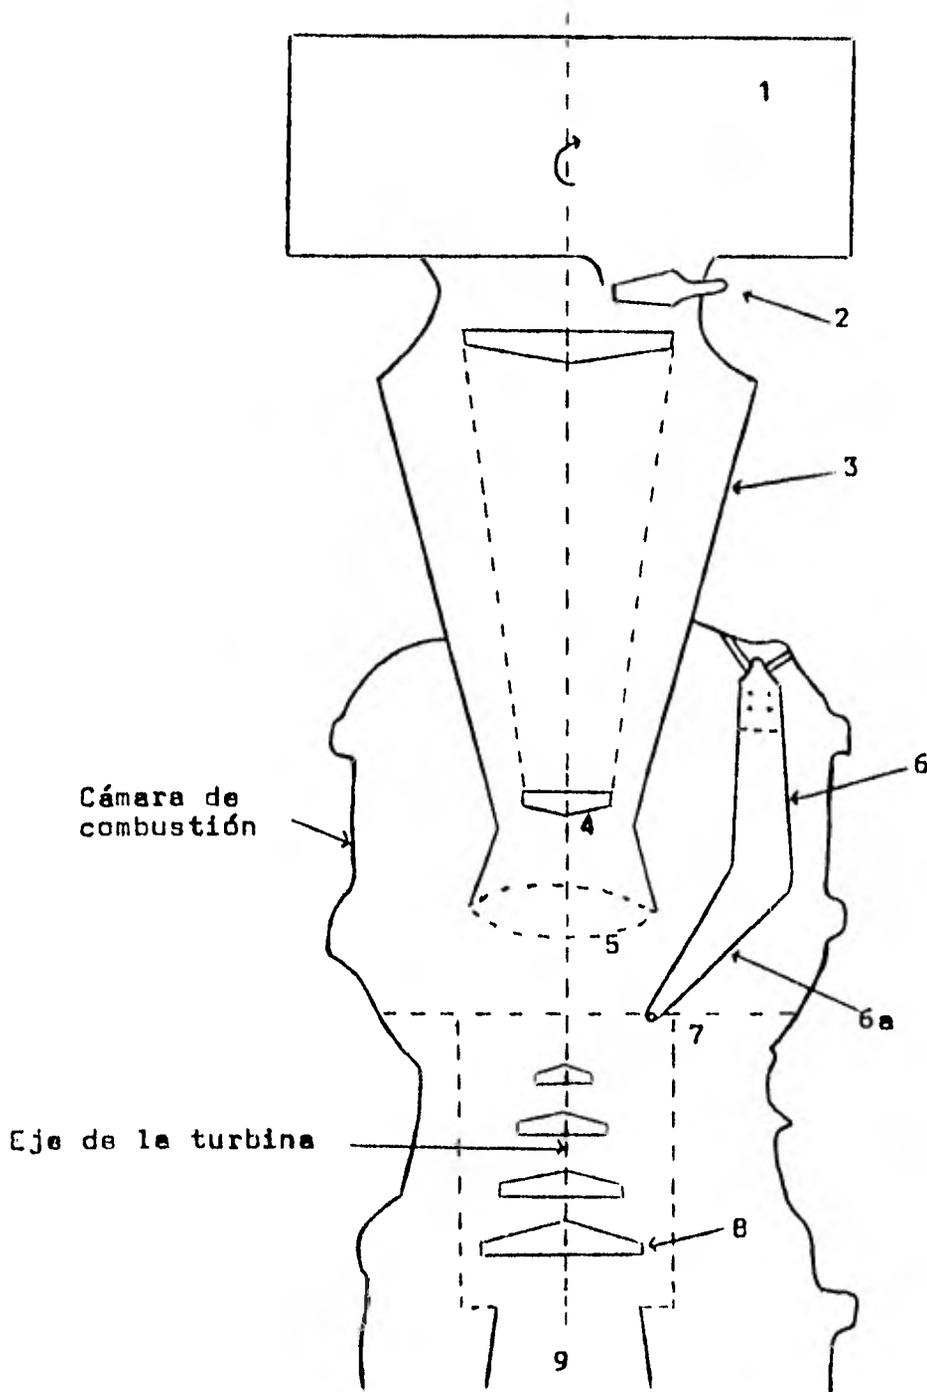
CORTE DE LA TURBINA WESTINGHOUSE TIPO W-501D.
